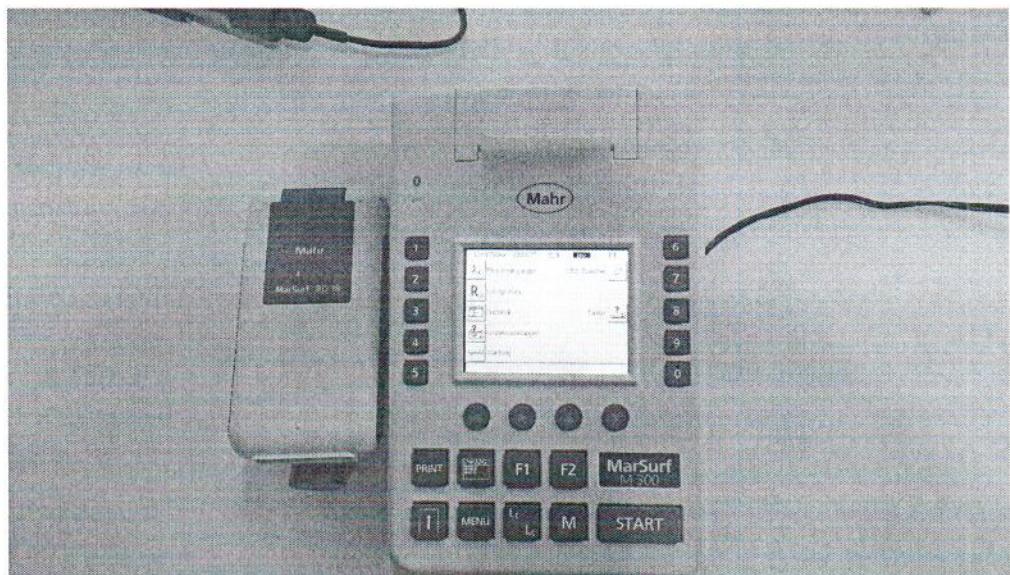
Внешний вид приборов для измерения шероховатости поверхности MarSurf M 300 в составе с RD 18
